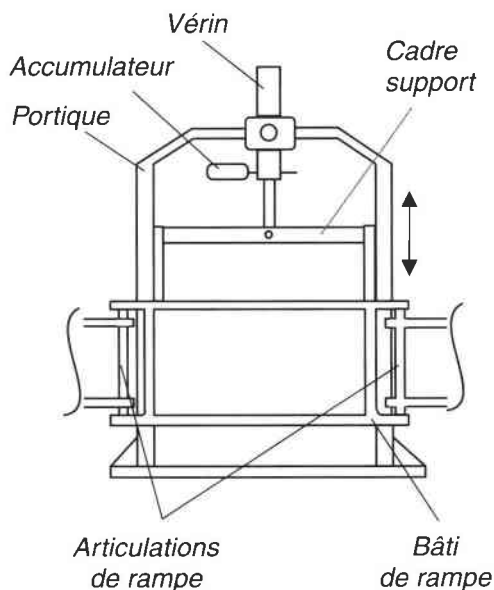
Exemple d'un montage de rampe sans dispositif de stabilisation
